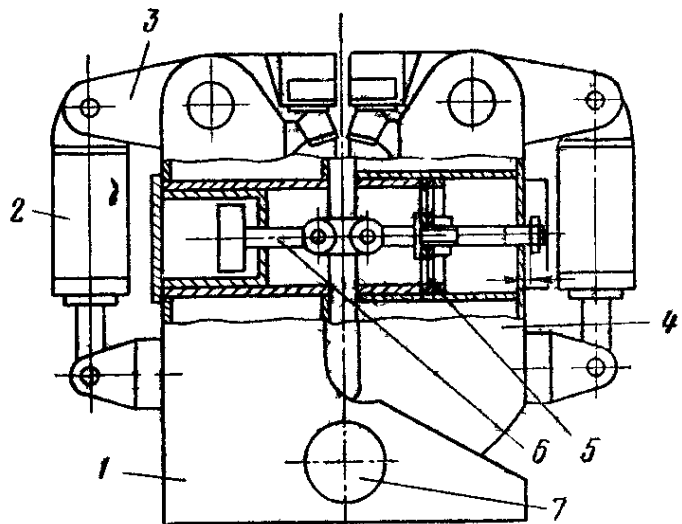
Машина К-617 для сварки импульсным оплавлением
